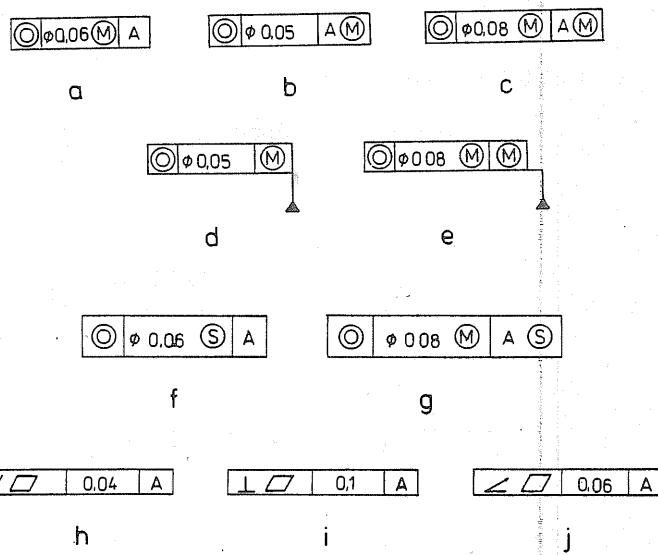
Vyplňovanie polí tolerančného rámčeka
